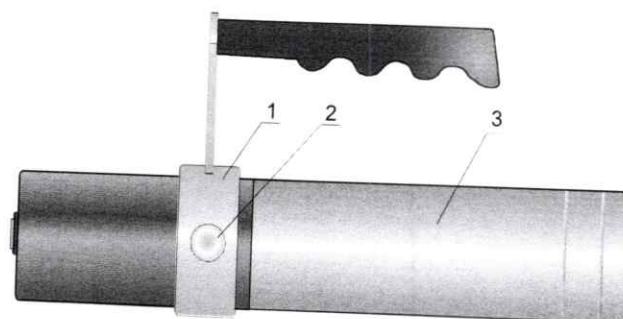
Vista Generale di PU2 montato sull'asta telescopica
